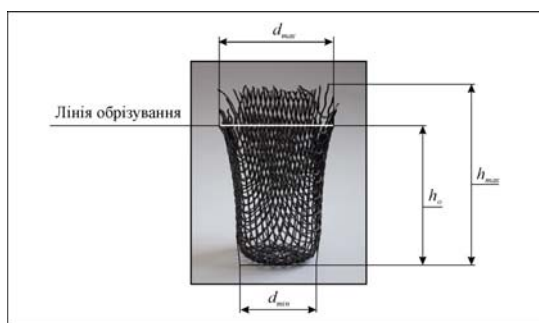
Друге витягування циліндричної деталі із металевої сітки
